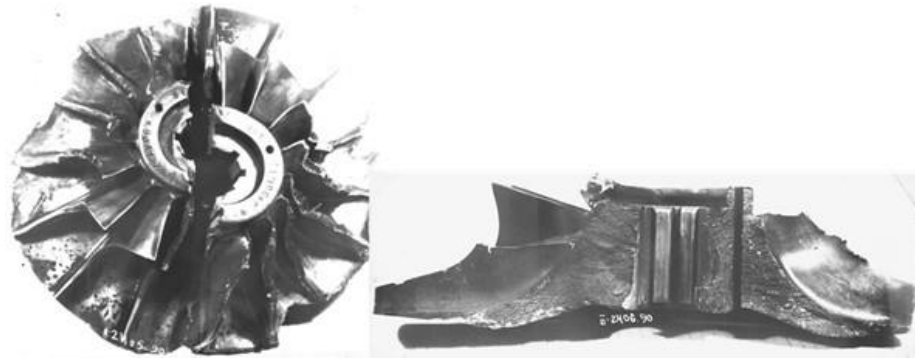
Общий вид разрушенной крыльчатки колеса насоса:
